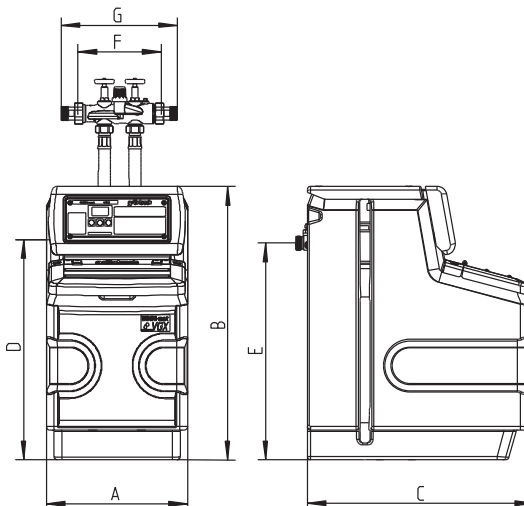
Чертеж с размерами установки умягчения WINNI-mat® VGX
